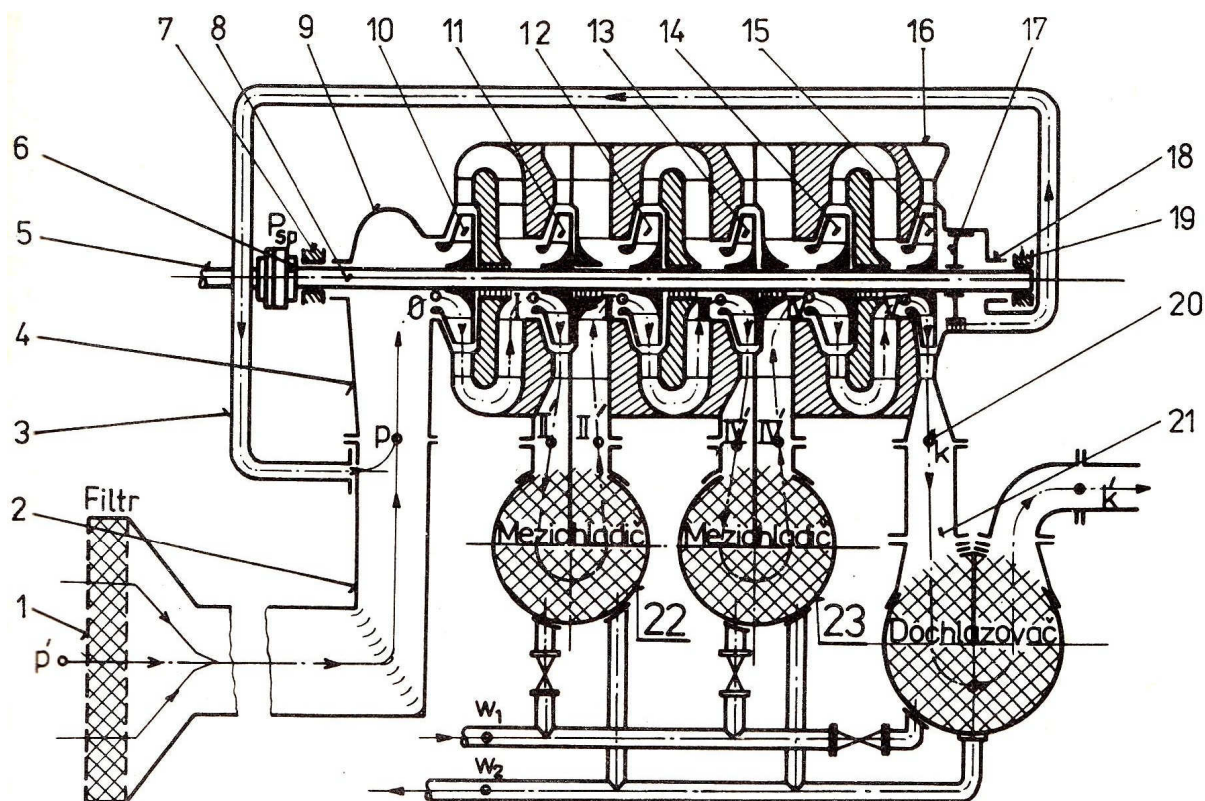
Volba měřících bodů – ložisko před a za turbínou
